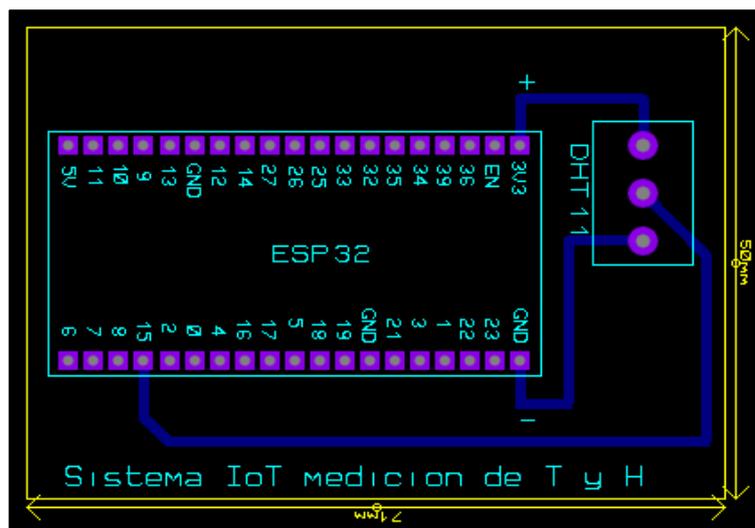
Diseño de PCB en Proteus v8.13. Fuente propia.
